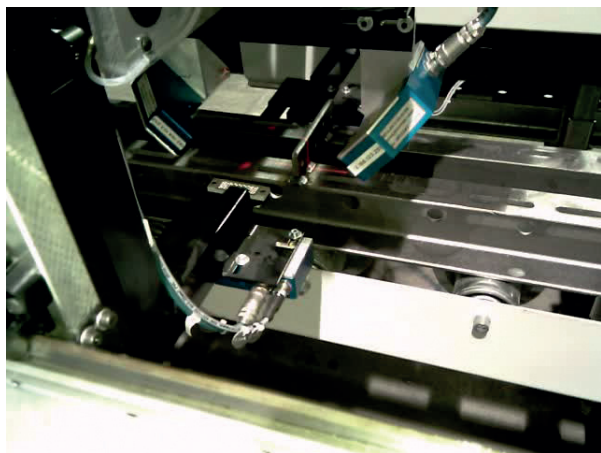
Schweißnahtkontrolle mit dem M2-iLan-Laserscanner der MEL (mit freundlicher Genehmigung der MEL GmbH)
